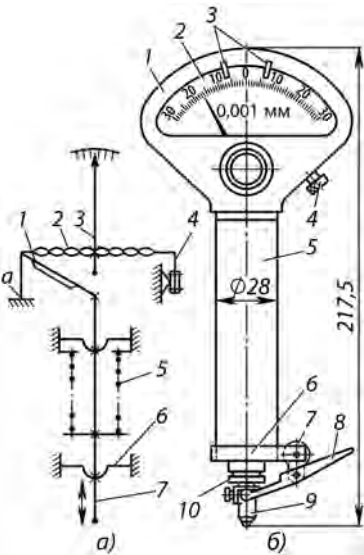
Пружинна вимірювальна головка ИГП:
